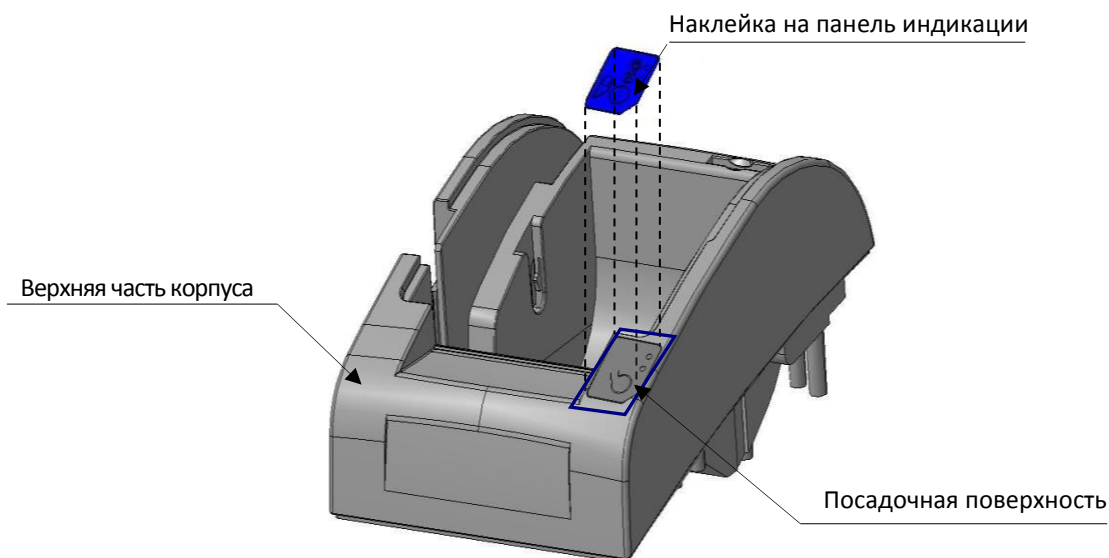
Посадочная поверхность верхней части корпуса изделия
